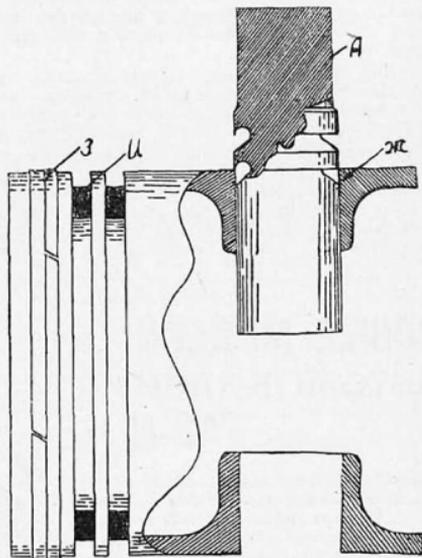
Обработка втулки верхней головки шатуна шарошкой
